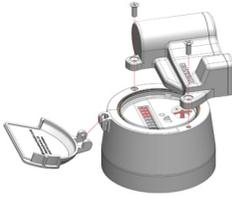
Montage des EDC-S auf Zähler mit Kupfer/Glas-Zählwerk (IP68)
